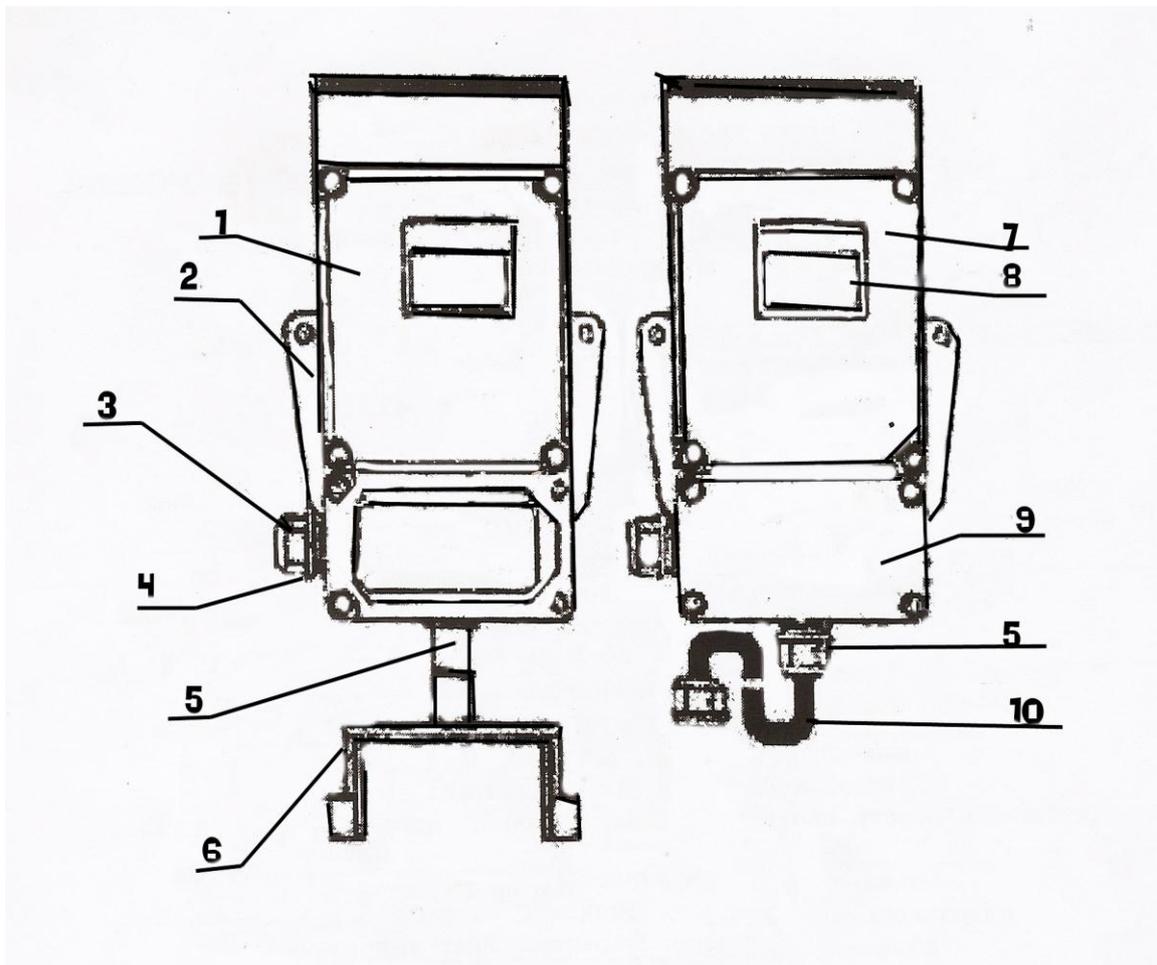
Вид прибора СДСВ 01: 1 – крышка аппаратной части; 2 – элементы крепления; 3 – кабельные вводы; 4 – плата внешней коммутации с клеммными разъемами; 5 – труба крепления измерительной головки к корпусу; 6 – измерительная головка; 7 – СДИ наличия питающего напряжения; 8 – ЖКД; 9 – крышка отделения кабельных вводов; 10 – кабель связи измерительной головки с датчиком; 11 – ручка для переноски
